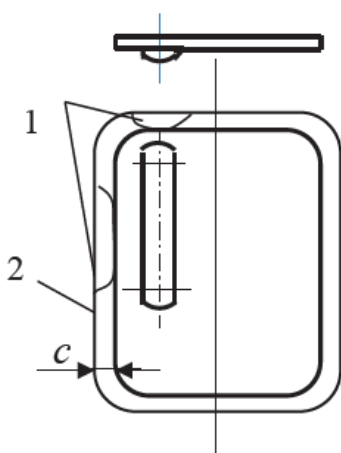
Искажение контура заготовки в связи с утяжкой материала при формовке ребра жесткости: 1 – утяжка, 2 – контур заготовки
